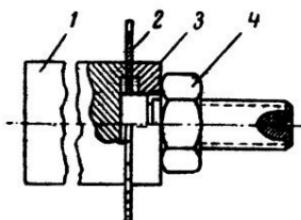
Оправка с дисковой фрезой для прорезания шлицев на токарном станке: 1 — оправка; 2 — фреза; 3 — шайба; 4 — гайка.
